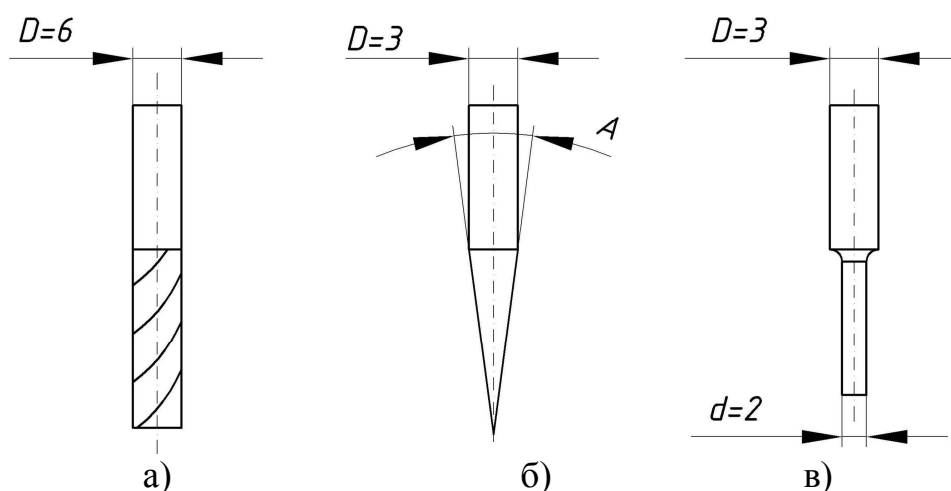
Концевые фрезы для фрезерования рельефного узора
